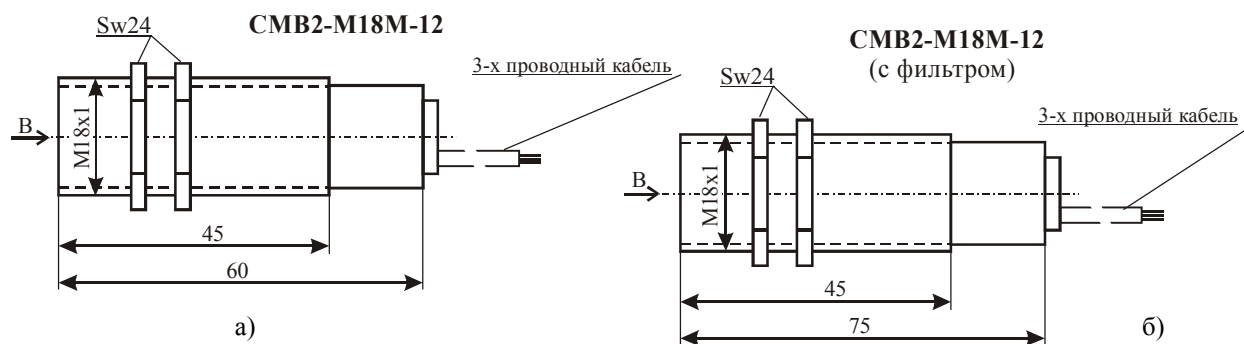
Внешний вид и габаритные размеры датчиков типа СМВ2-М18М-12: а – без фильтра; б – с фильтром
